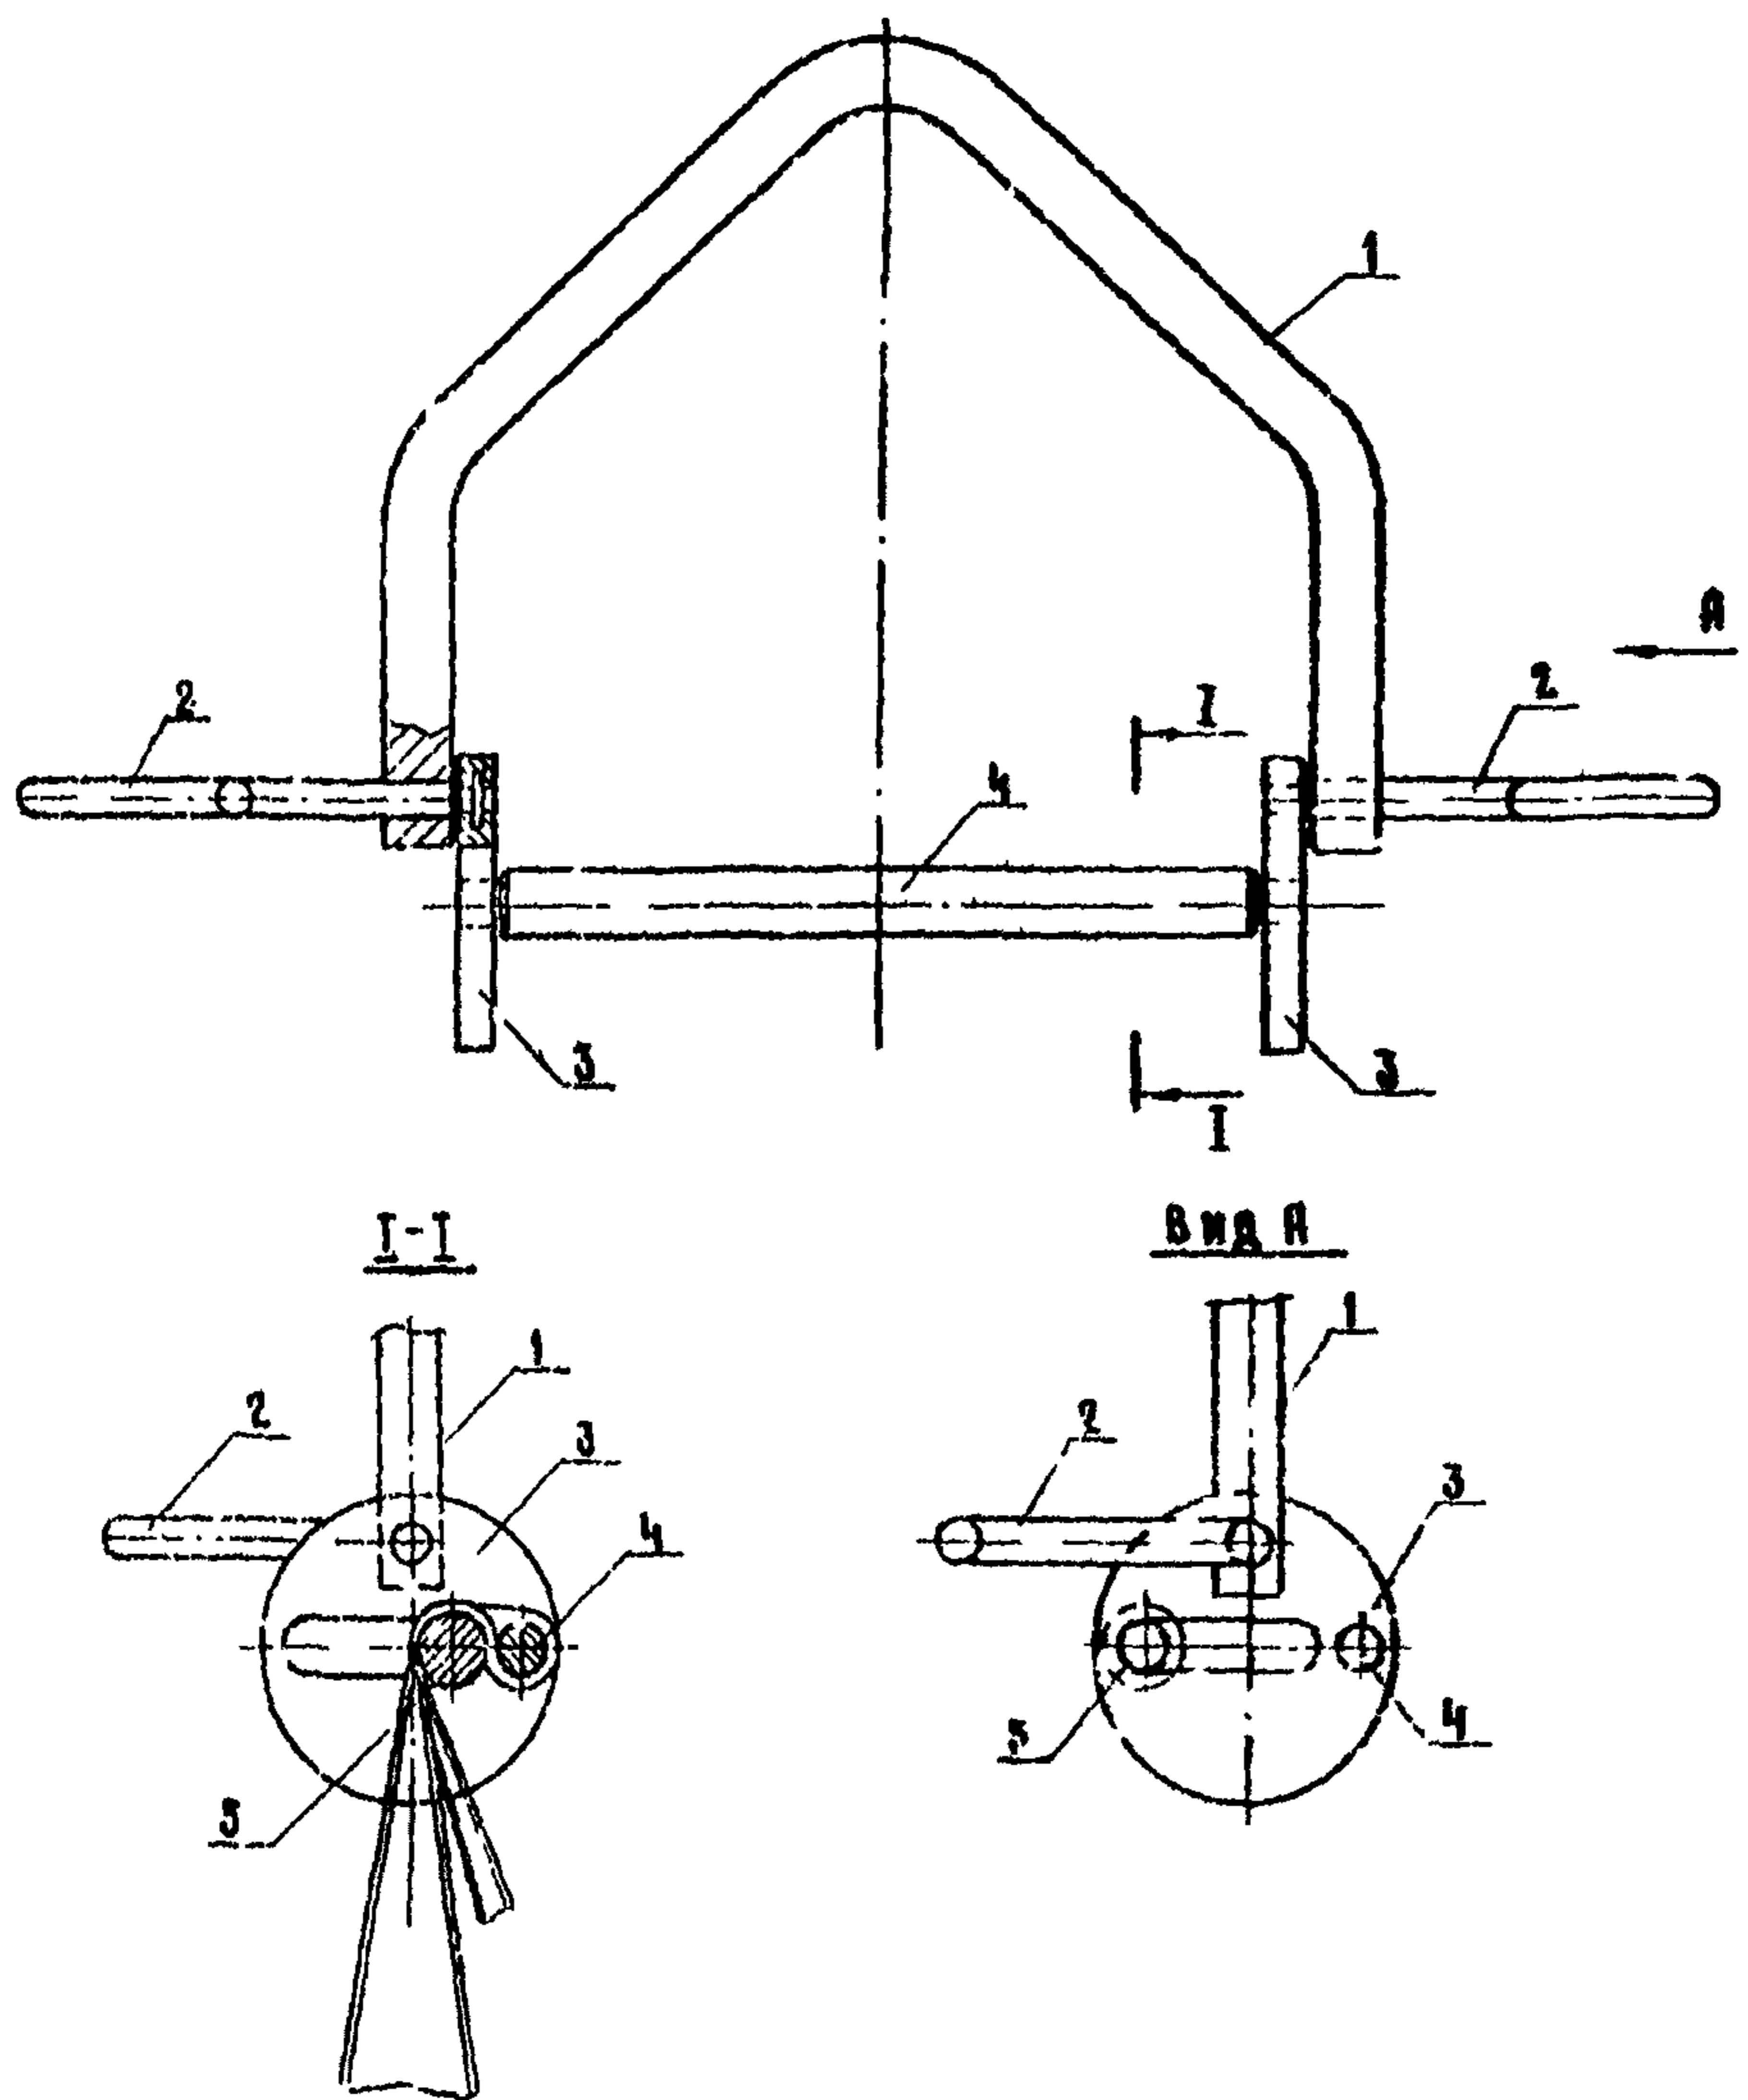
Грузозахватное приспособление с полуцилиндрической запаоюкой горловины контейнера: 1 - бугель; 2 - рукавка; 3 - диск; 4 - неподвижная штанга; 5 - подвижная штанга
